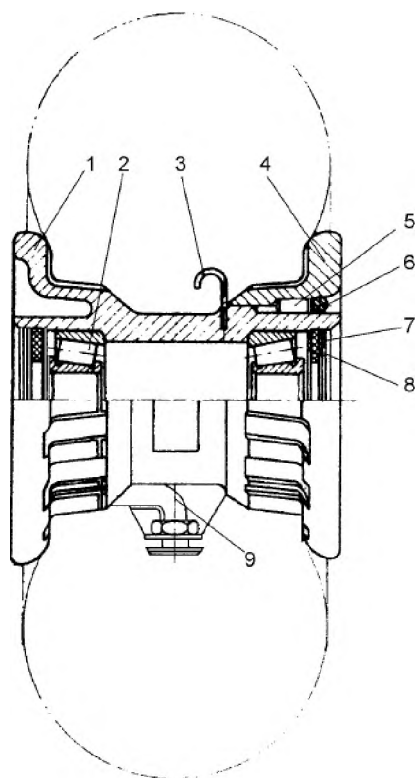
Устройство колеса передней стойки шасси вертолета Ка-26 [3]:
